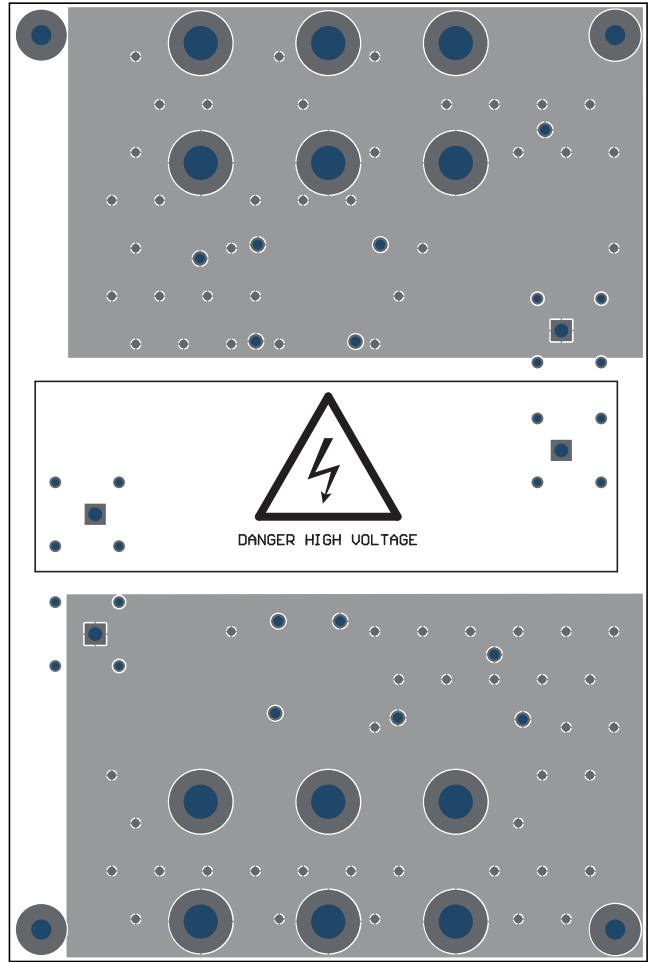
RES60EVM PCB 复合视图 ( 底视图 )
